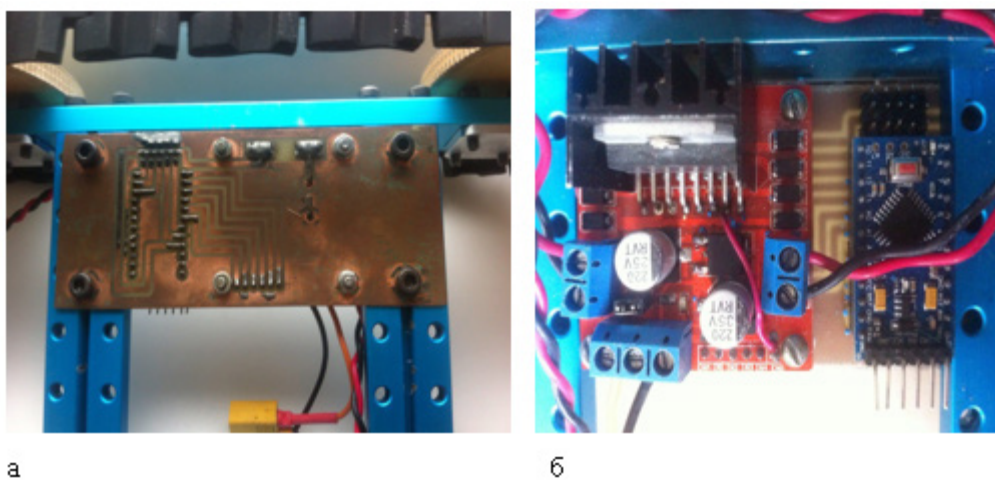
Печатная плата: а — Вид сверху, б — Вид снизу
